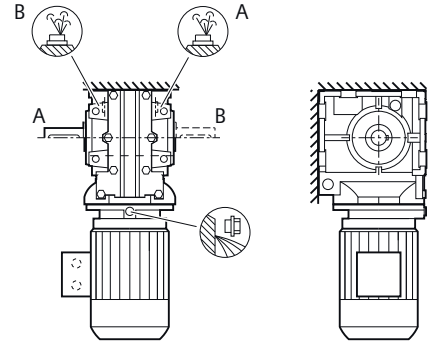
Salyangoz tipi düz dişli için montaj pozisyonları CF Flanşlı model ve CAZ gövde flanşlı, boyut 39 - 89
